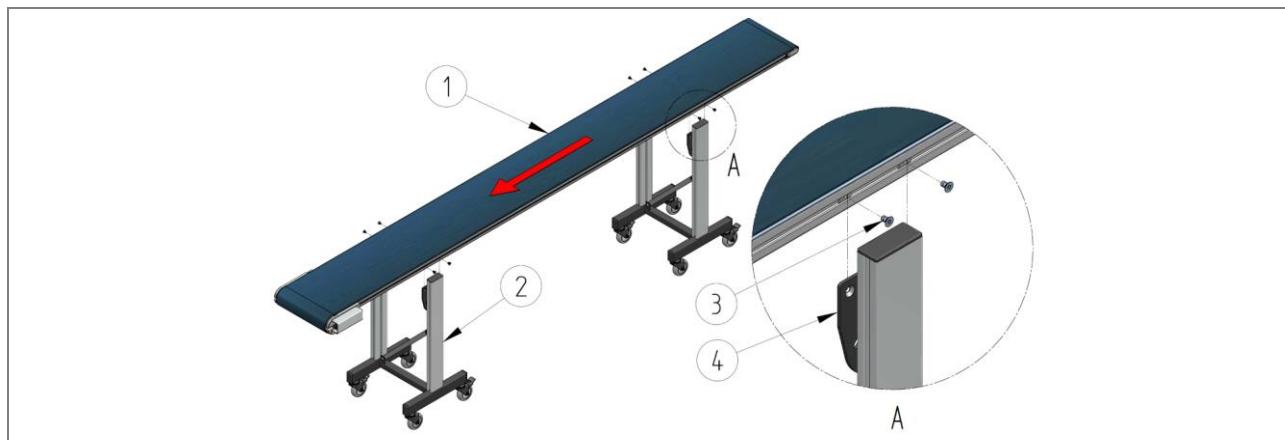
HE 060/ HM 590 alt şasisinin montajı
